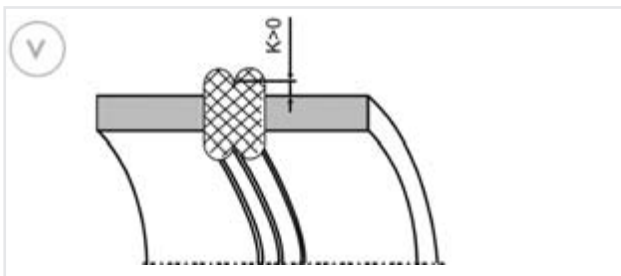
Soudure bout-à-bout avec un trop grand cordon de soudure (acceptable)
